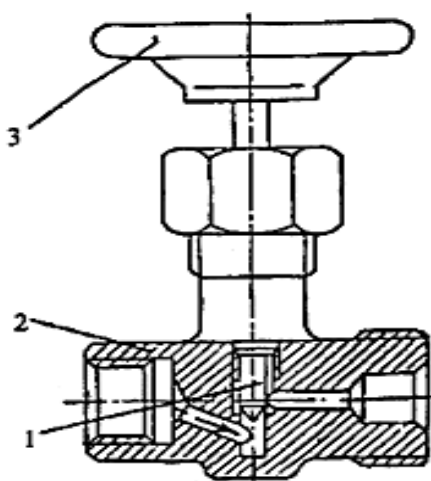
а. - Вентиль запорный игольчатый:
